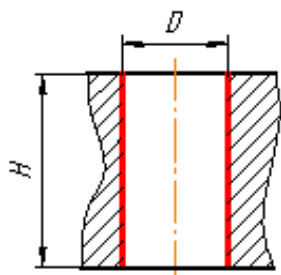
КТЭ цилиндрическое отверстие простое сквозное для поверхностей №20, 39
